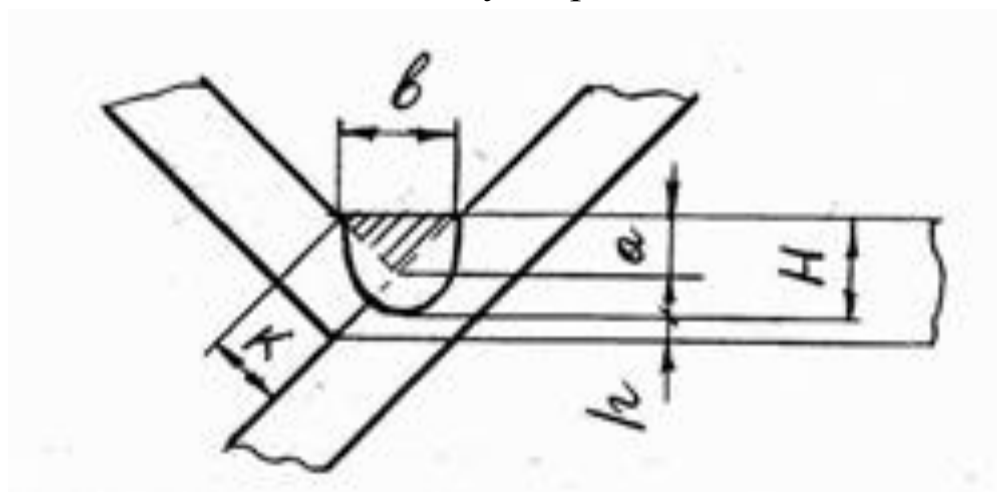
Конструктивні елементи кутового шва при зварюванні в «ЧОВНИК»
